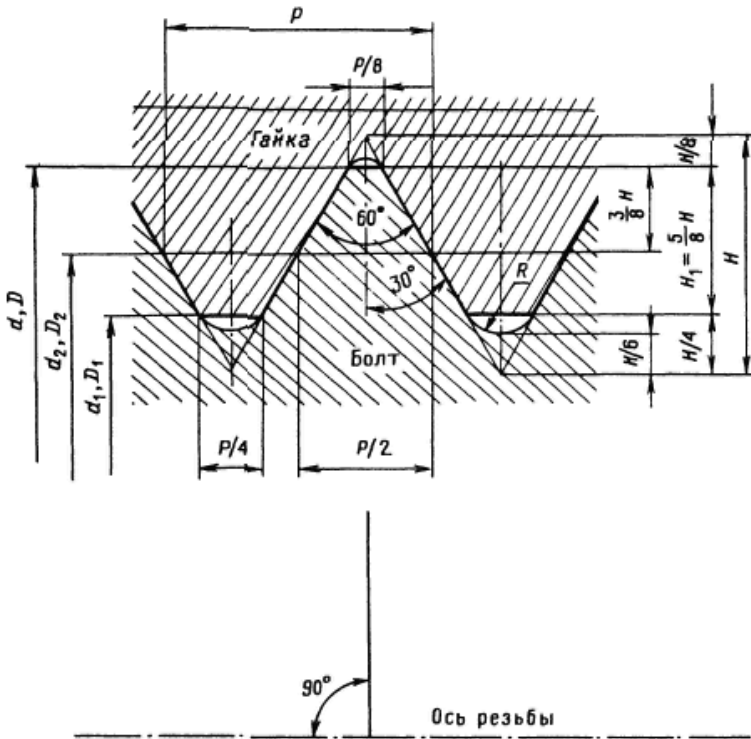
Основные размеры метрической резьбы: гайка- внутренняя резьба, болт- наружная резьба
